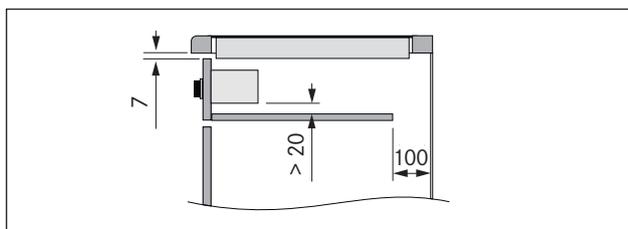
Vista laterale piano di protezione cavi e aerazione
